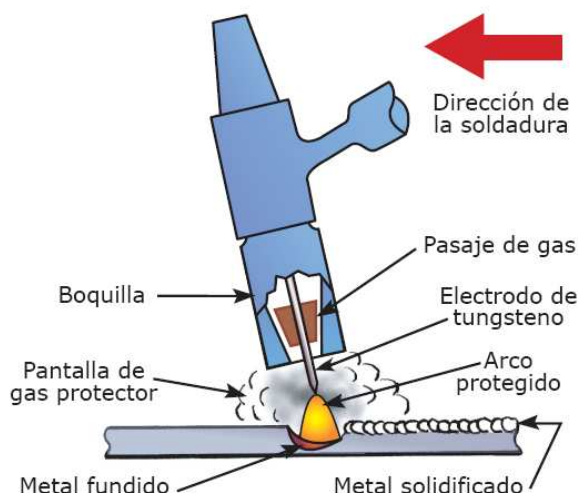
Esquema del proceso de soldadura TIG
